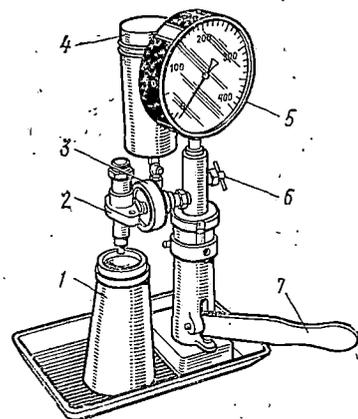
Проверка и регулировка форсунки на приборе КИ-562. (КП-1609А):
